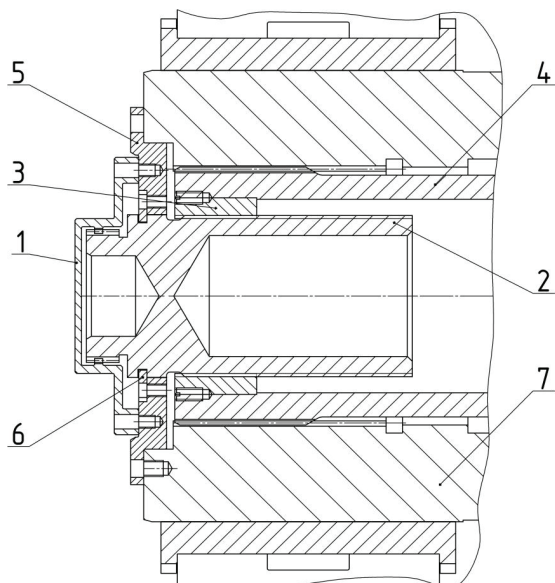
Механизм переключения редуктора: 1 – фланец шлицевой; 2 – втулка шлицевая с многозаходной резьбой; 3 – обечайка с многозаходной резьбой; 4 – торсионный вал; 5 – фланец фиксирующий; 6 – упорное кольцо; 7 – цапфа зубчатого колеса
